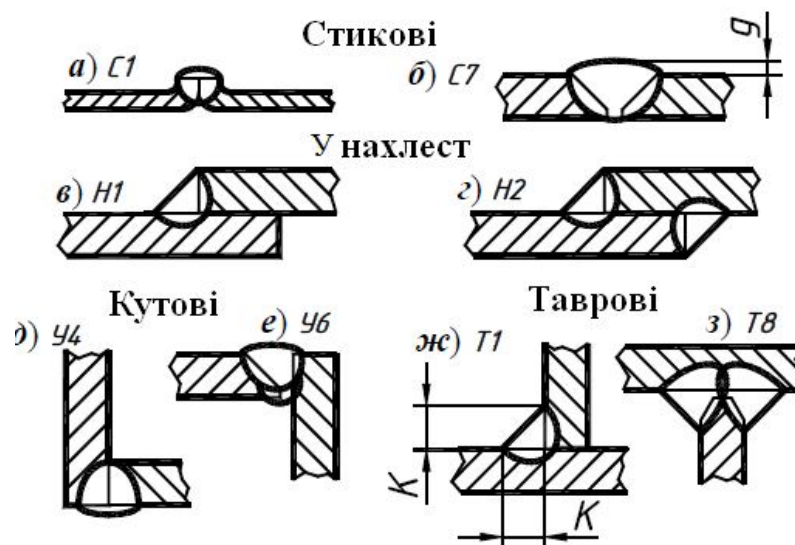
Види конструктивних з'єднань деталей зварюванням
